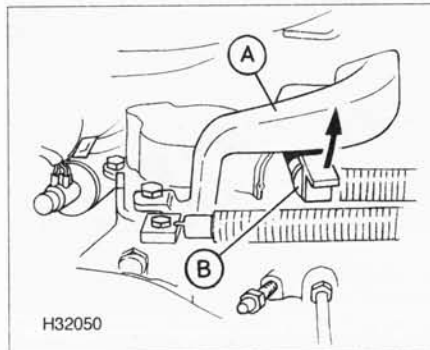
Рычаг троса выбора передач (B) и противовес (A) — коробка передач 02J
